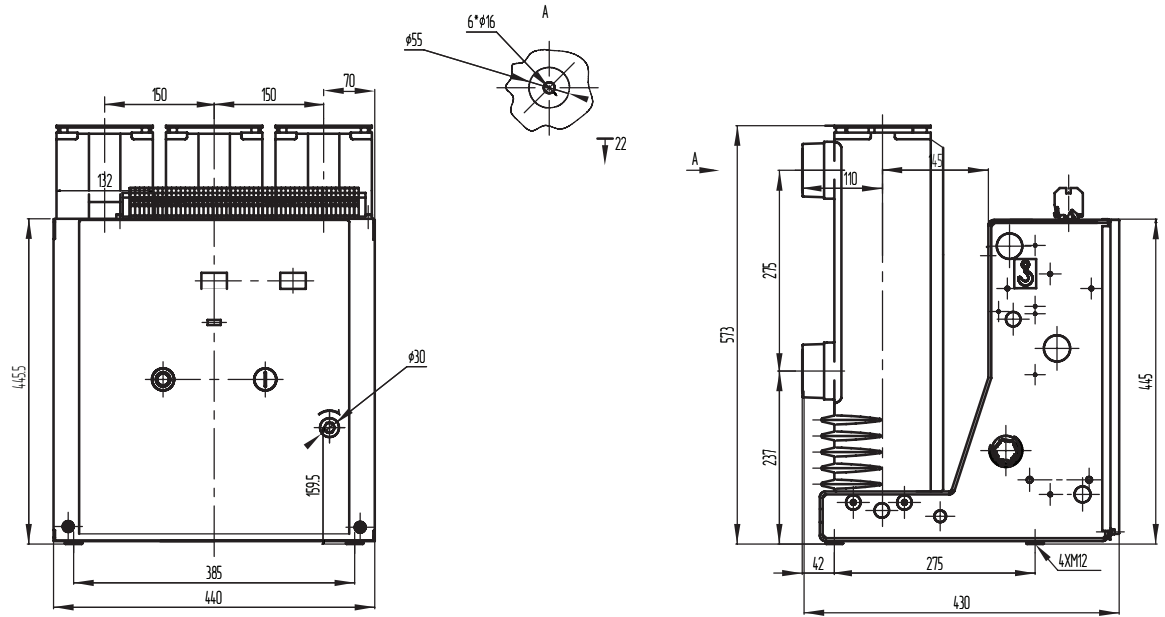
Габаритный размер выключателя ВВ-12 стационарного исполнения для ячейки шириной 800 мм
